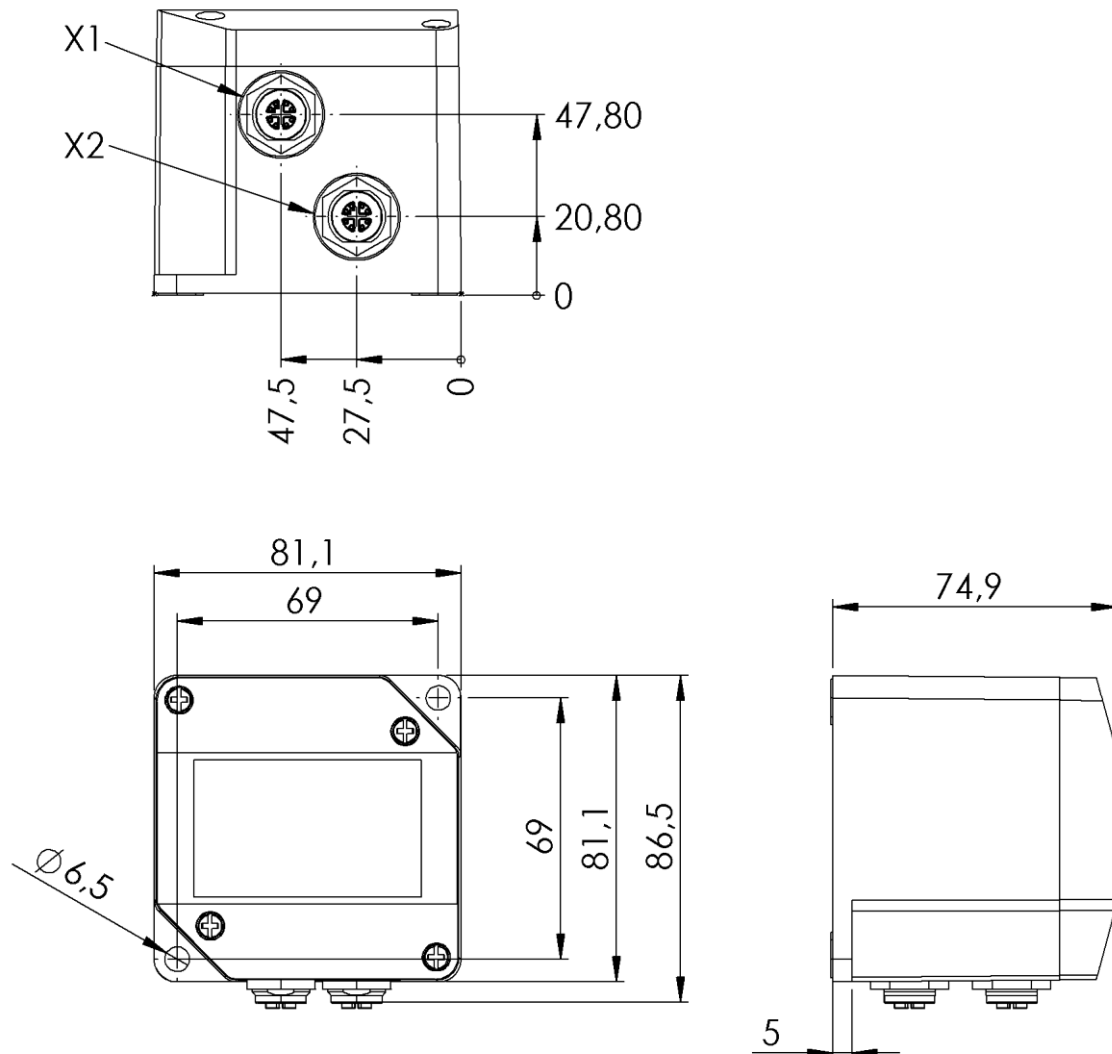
Maßzeichnung EN-95. Alle Maßangaben in Millimetern.
